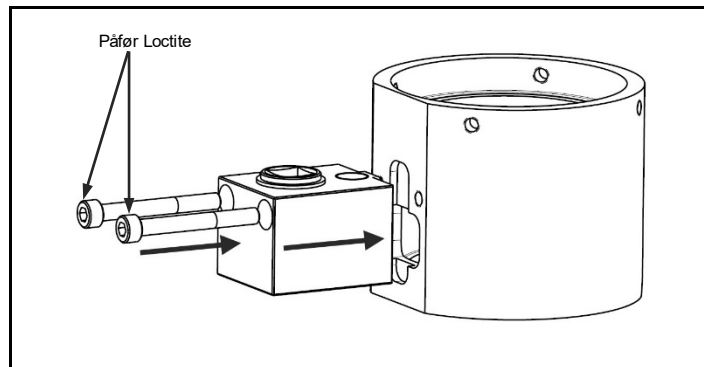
Kom Loctite på maskinskruerne, fastgør samlet gearkasse på bro
